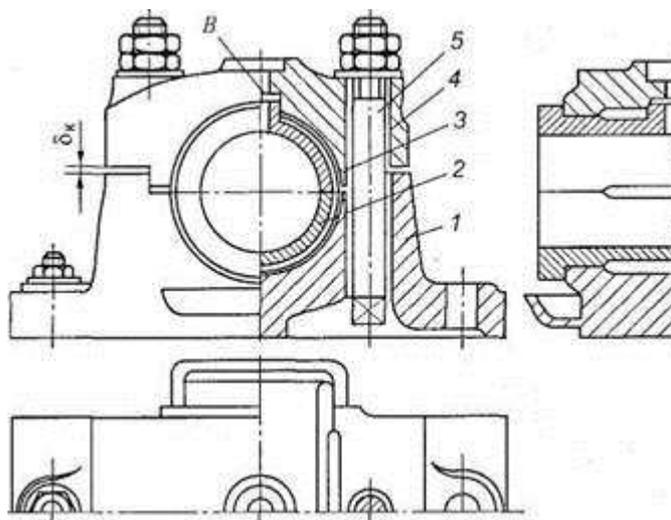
Разъемный подшипник скольжения: 1 — станина; 2, 3 — вкладыши (полукольца); 4 — крышка; 5 — болт
